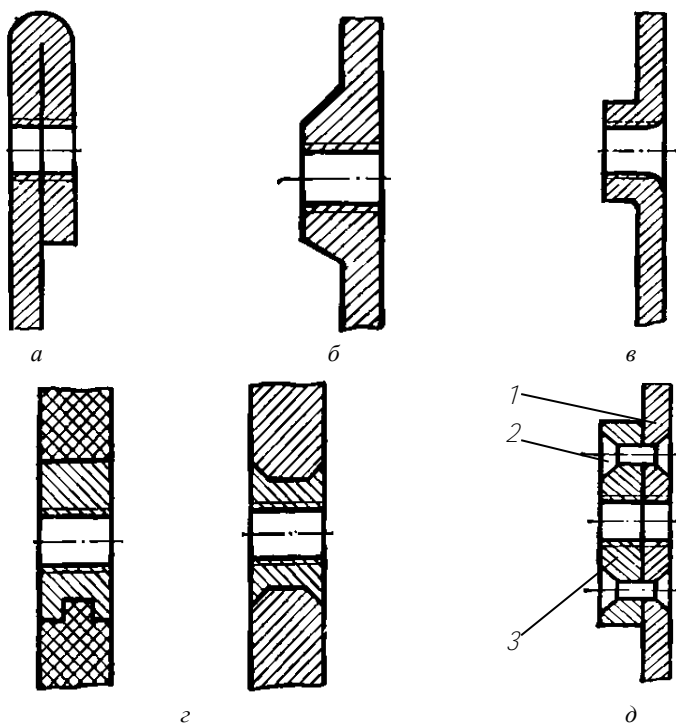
Способы увеличения длины резьбовой поверхности:
